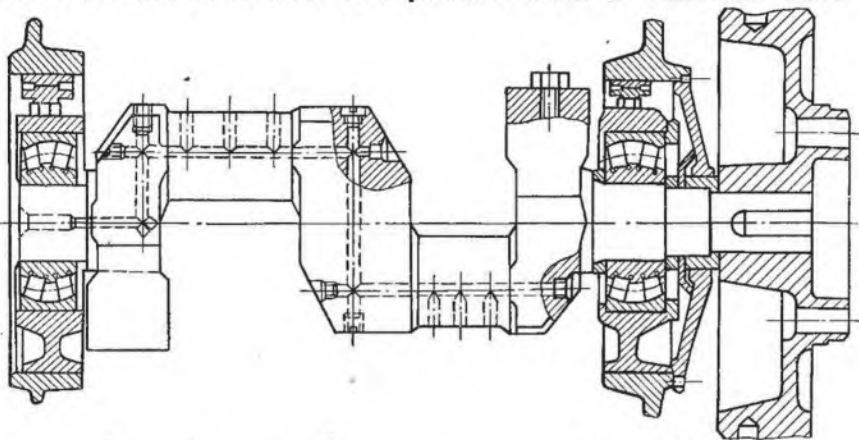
Конструкция двухопорного коленчатого вала многорядного компрессора
